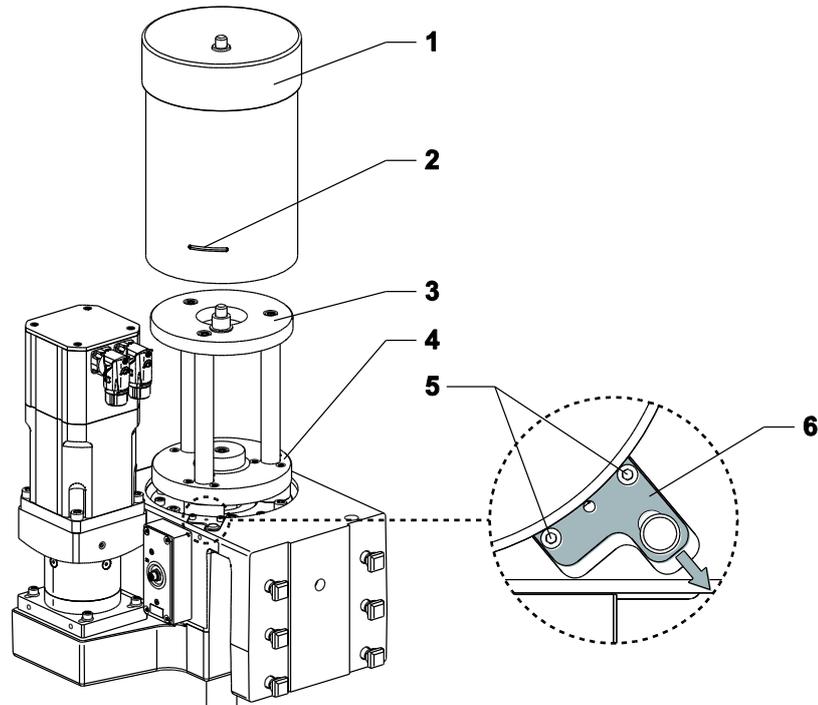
Nettoyer la plaque de guidage ElectricPress 347
